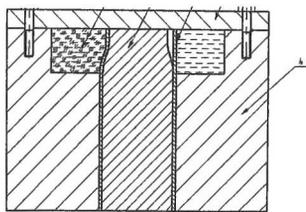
Штамп для обжима трубчатой заготовки с использованием энергии расширения воды при ее заморозке
